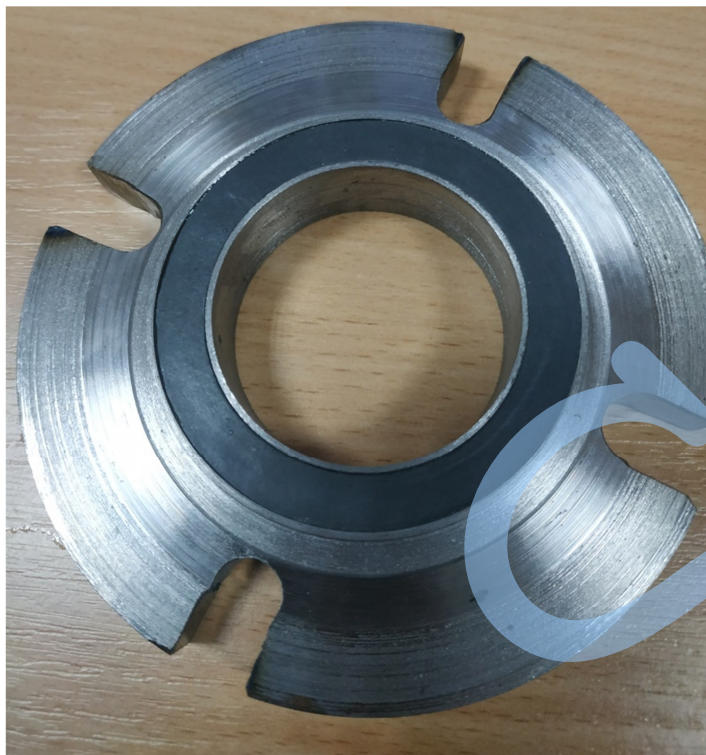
Торцева поверхня кільця ущільнення виготовленого з ПТФЕ композиту
